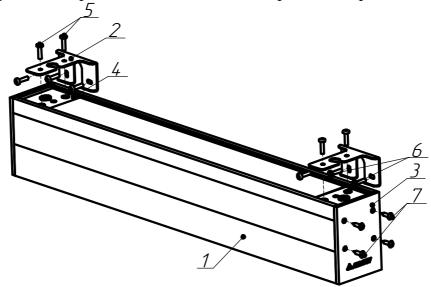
а - Схема крепления светильников ДПО02 Up/Down к стене 1- светильник, 2- кронштейн для настенного крепления ДПО02 Up/Down, 3- торцевая крышка, 4- пластина, 5- винт крепления, 6- саморезы для крепления к стене, 7- саморезы для крепления крышек
